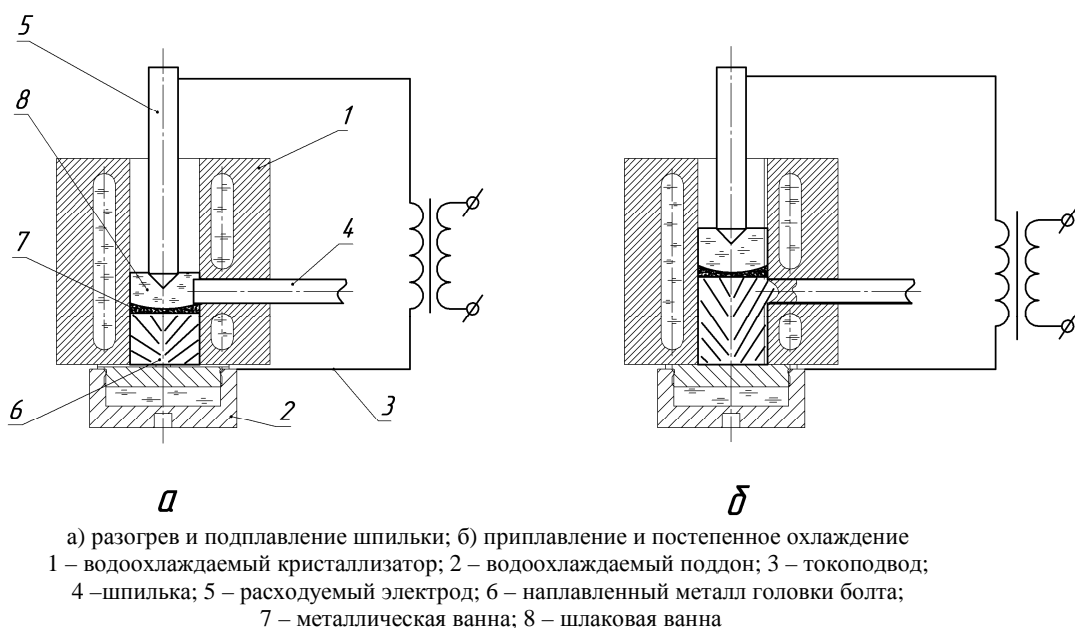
Схема получения заготовки спецболта методом электрошлакового приплавания
